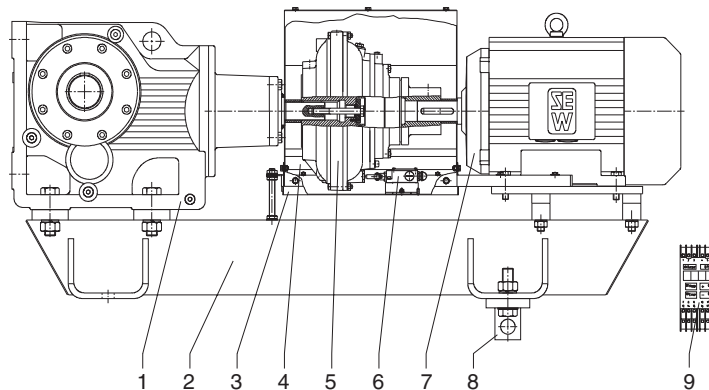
Konstrukce pohonu s hydraulickou rozběhovou spojkou a brzdou BM(G)
